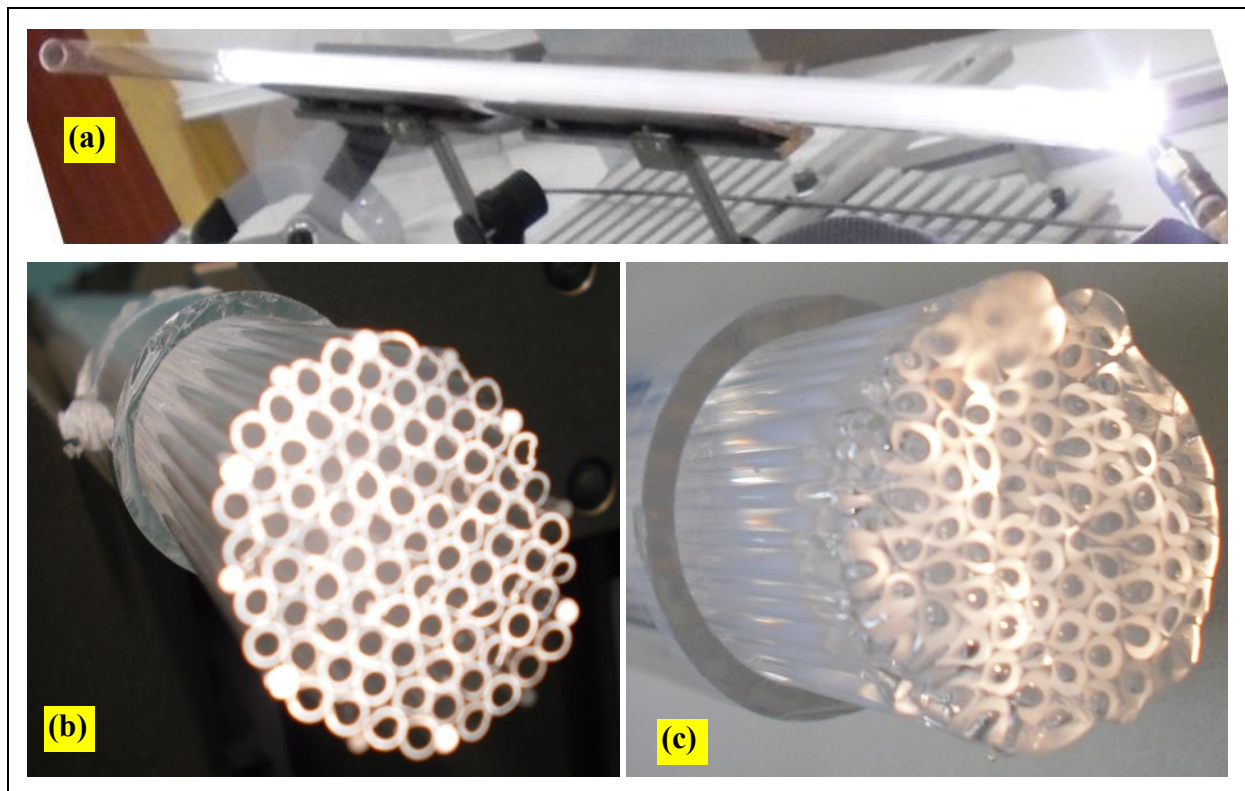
(a): soudure des capillaires, (b): l'état initial avant la soudure, (c): l'état final après la soudure
